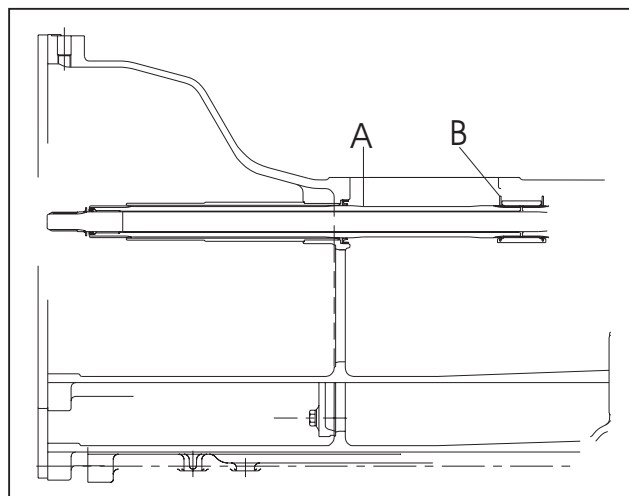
Séparer le carter de boîte avant du carter de boîte arrière.
